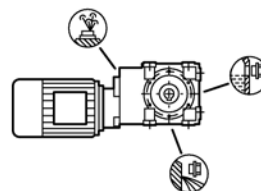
Bauformen für B. Baugrößen 28 - 38 ohne zusätzliche Verschlusschraube
